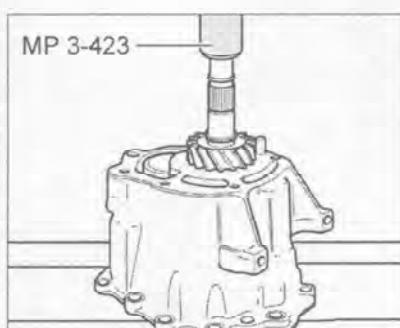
Спрессуйте шестернию 6-й передачи.
